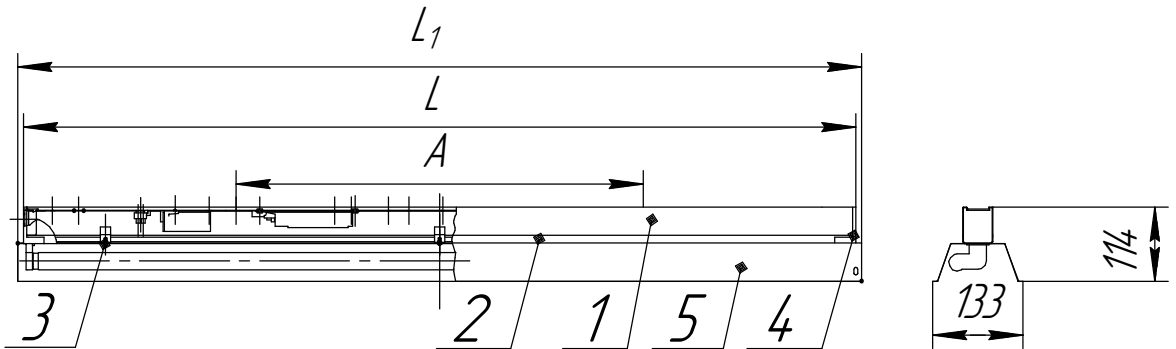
1. Корпус в сборе, 2. Крышка, 3. Винт, 4. Крышка, 5. Отражатель.
